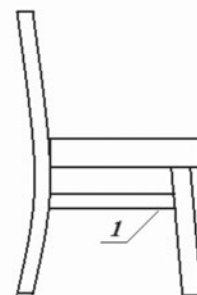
Стул с усиленной конструкцией: 1 – распорка
